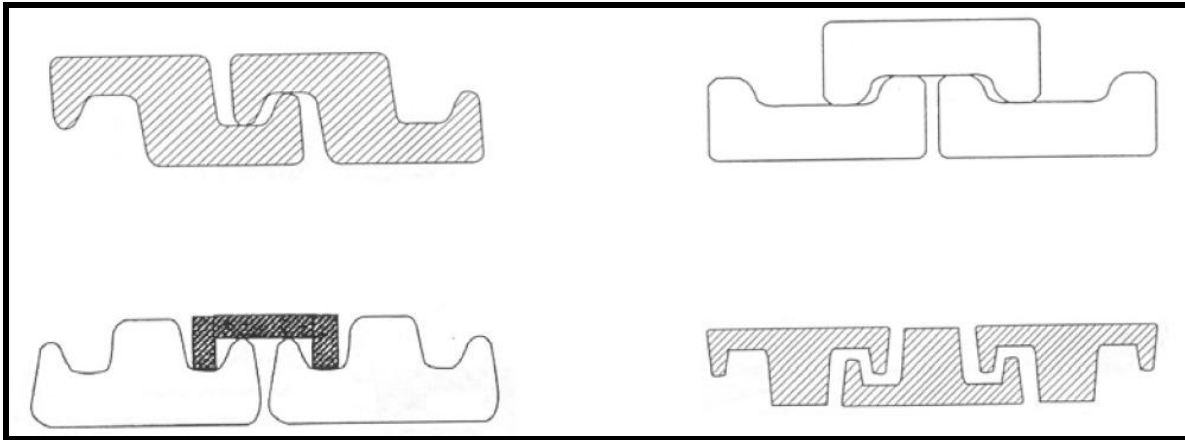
Tipos de perfis utilizados nas armaduras de pressão: Perfil Z, Perfil C, Perfil T com grampo e Perfil T. (API RP 17B, 1998)
